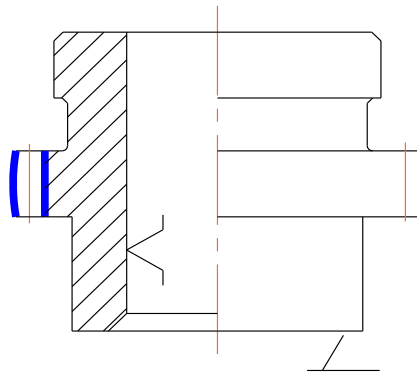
Умовна схема базування при фрезеруванні зуб'їв
